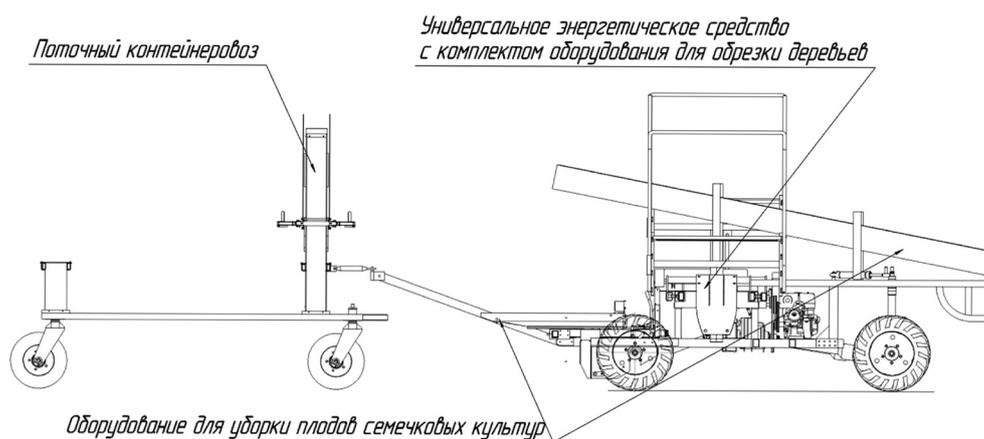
Общий вид самоходной плодуборочной платформы с контейнеровозом
